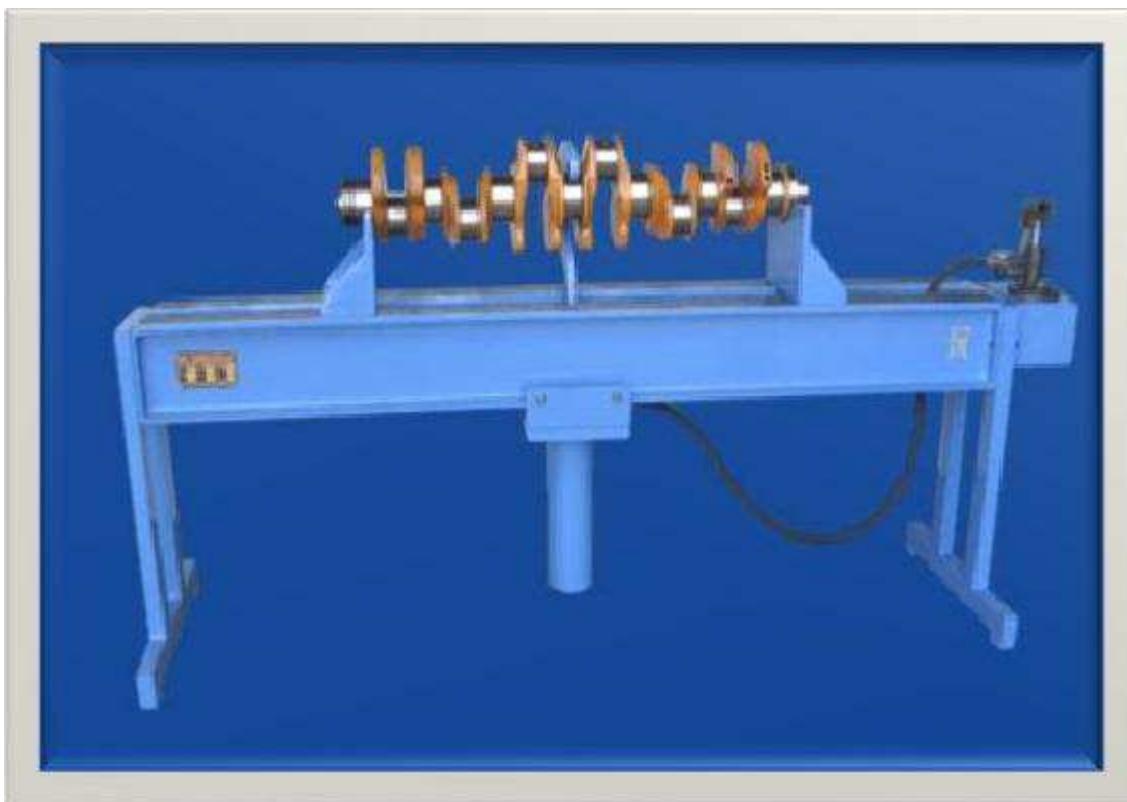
Гидравлический пресс для правки коленвалов KDP 1800
